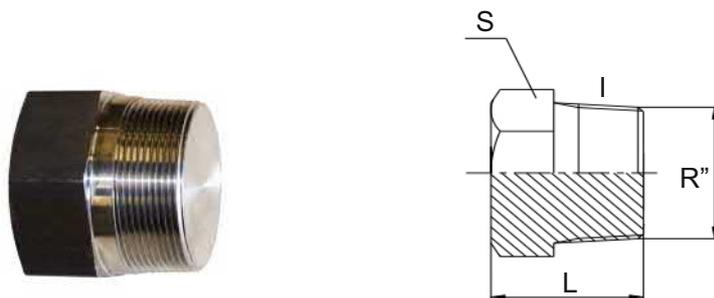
Заглушка для установки на выпускном трубопроводе вместо РВД
